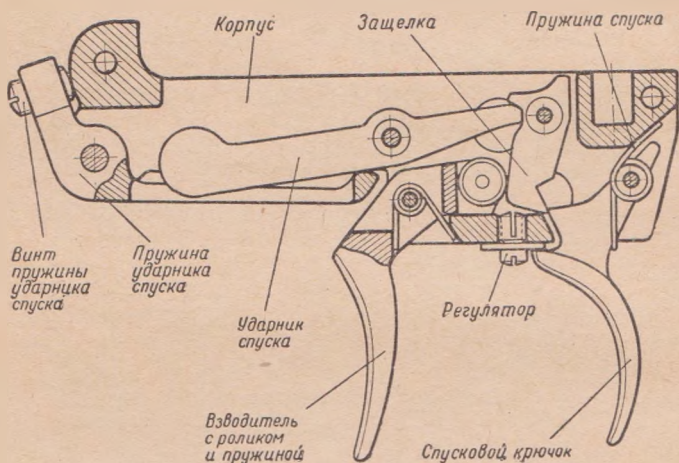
Ударно-спусковой механизм винтовок „Стрела“, „Зенит“, „Тайга“
